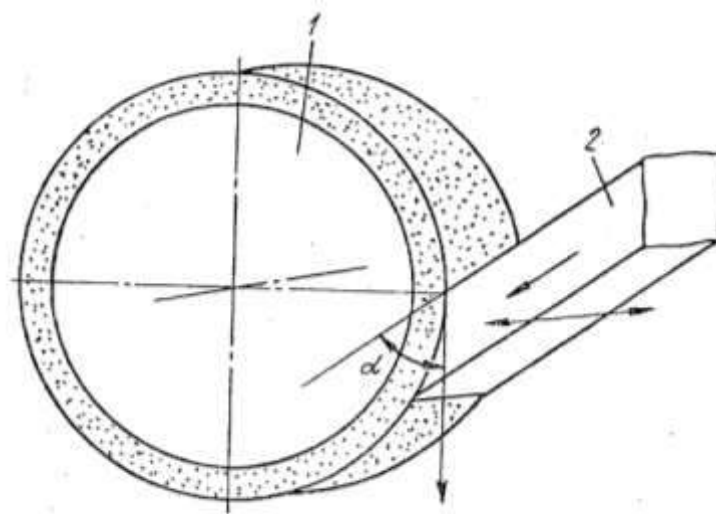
Схема правки свободным абразивом с движущимся возвратно-поступательно притиром [9]
